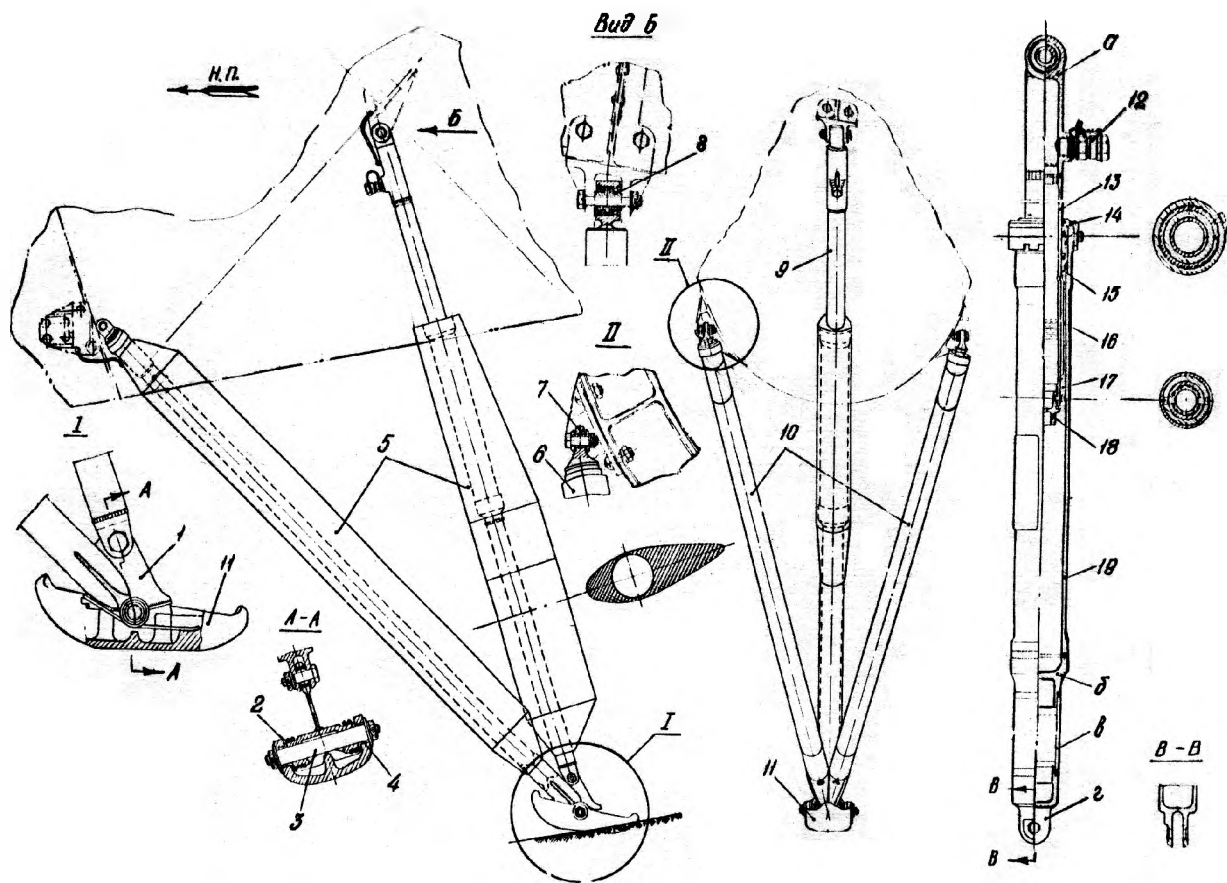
Конструкция хвостовой опоры вертолета Ми-24А [13]:
